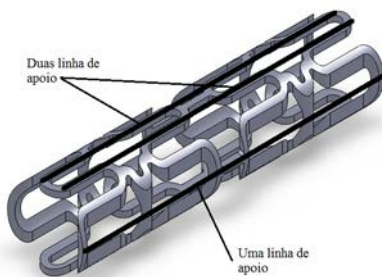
Linhas de apoio das placas durante ensaio de compressão no plano 1 e 2 do *stent*.
